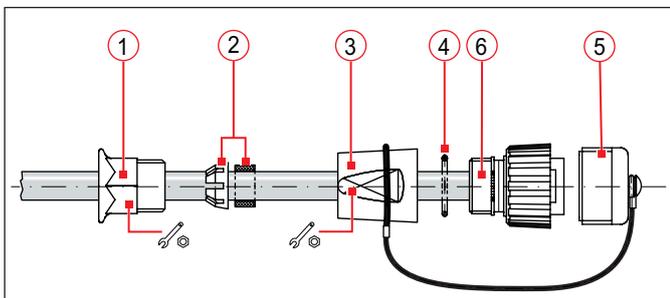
Beispiel für Stecker mit Gewinde, Endgehäuse und Verschraubung (gilt analog auch für Dosen mit Gewinde)
